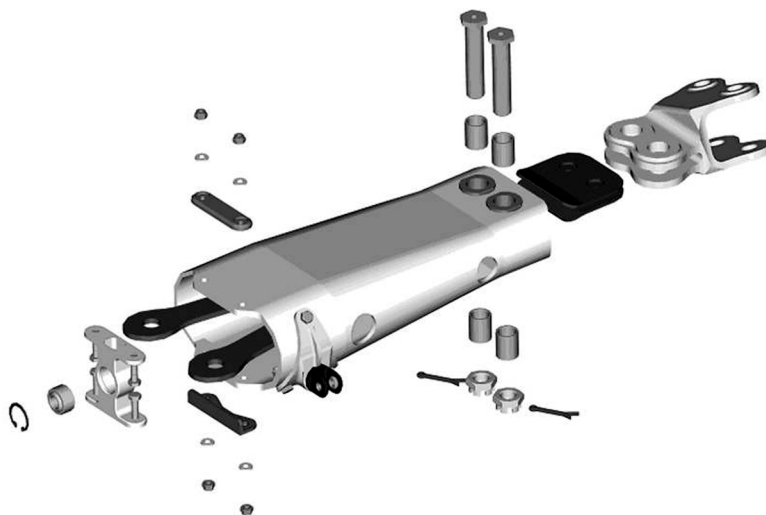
Рукав торсиона несущего винта с вилкой крепления лопасти
